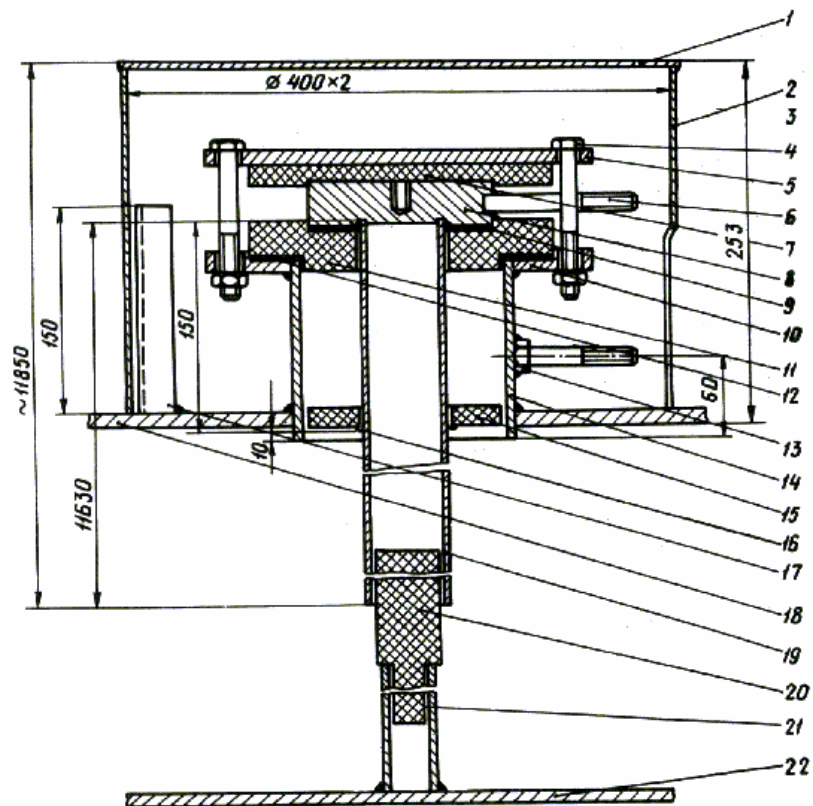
Узел катода хранилища амводы: 1 - кожух для защиты от атмосферных и механических воздействий; 2 - обечайка кожуха; 3 - болт (шпилька); 4 - гайка; 5 - фланец верхний (X18H10T); 6 - шпилька для подключения кабеля (X18H10T); 7 - прокладка изолирующая верхняя (текстолит)- 8 - фланец катода (X18H10T); 9 - прокладка уплотнительная (паронит, резина); 10 - фланец штуцера (X18H10T); 11 - прокладка изолирующая (текстолит); 12 - прокладка уплотнительная (паронит, резина); 13 -- шпилька для подключения кабеля (X18H10T); 14 - штуцер; 15 -кольцо центрирующее (текстолит); 16 - кольцо стопорное (X18H10T); 17 - стойка установочная; 18 крышка хранилища; 19 -катод (X18H10T); 20 - фиксатор (фторпласт); 21 - втулка фиксатора (X18H10T); 22 - днище хранилища.
